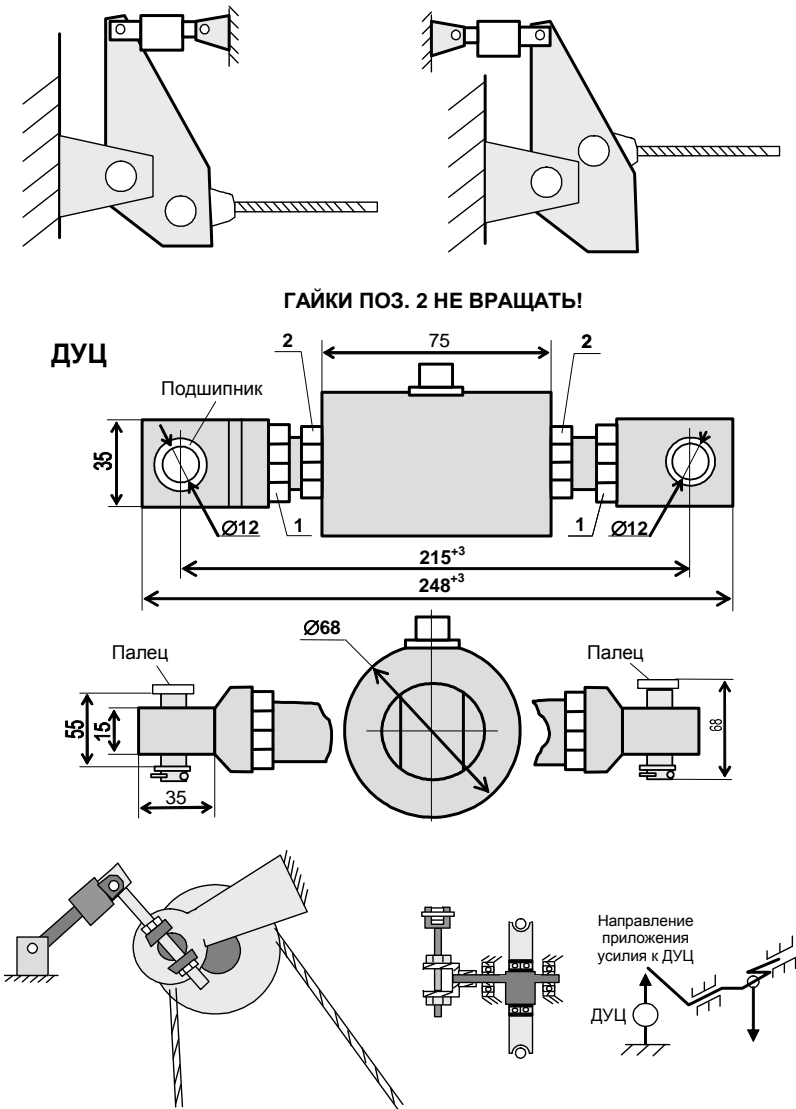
Габаритные и присоединительные размеры ДУЦ
